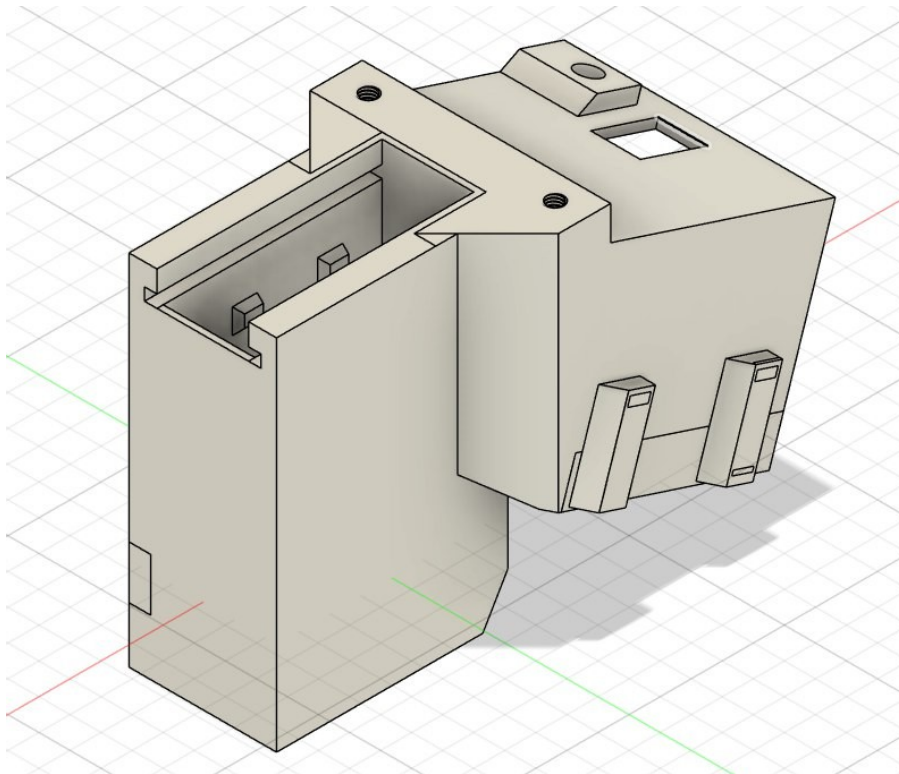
3D-модель защитного корпуса с системами вентиляции и продува
